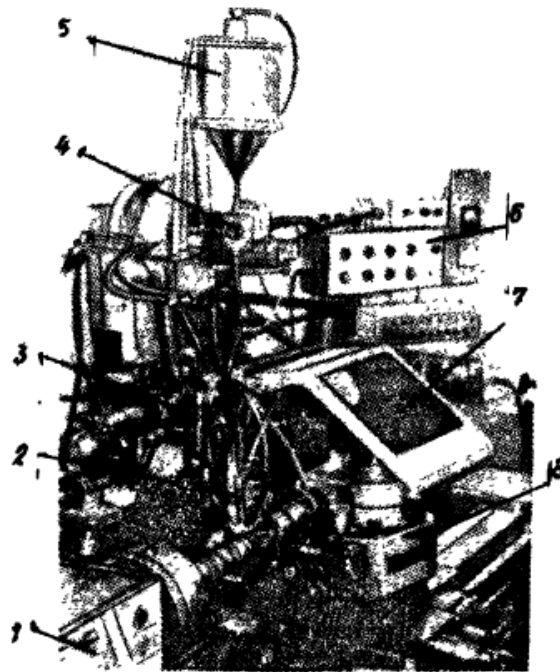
Загальний вигляд модернізованої установки ППНМО: 1 - токарний верстат; 2 – плазмотрон; 3 - маніпулятор; 4 – дозатор; 5 – бункер; 6 – пульт управління; 7 – екран; 8 – фрезерна головка.
